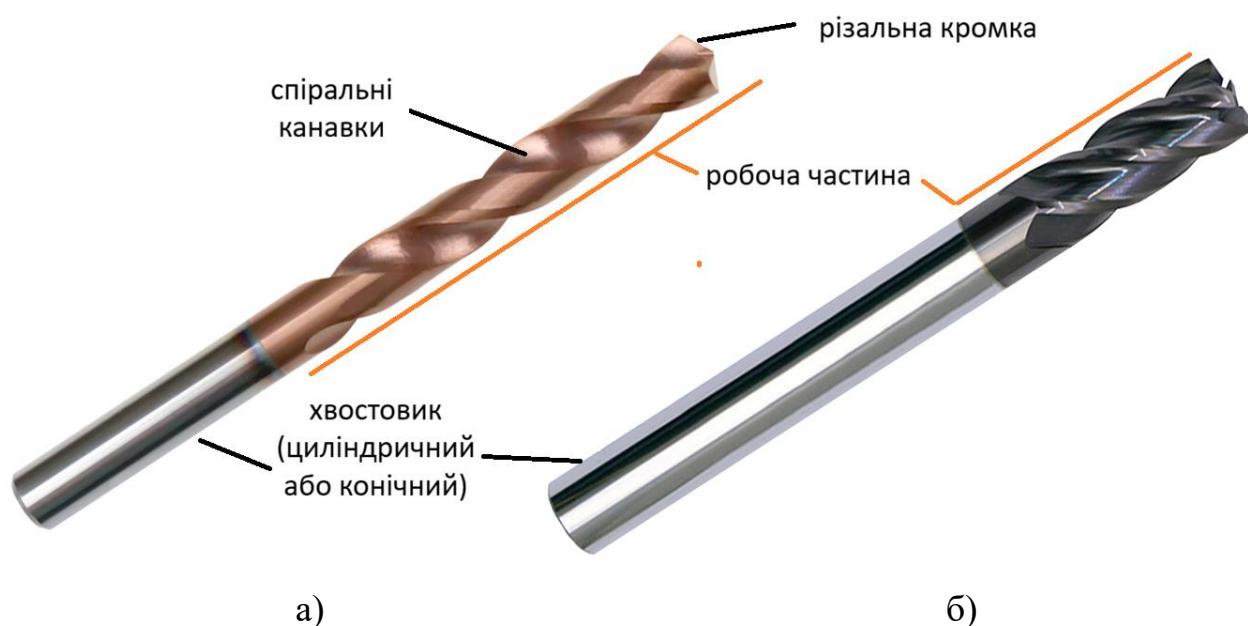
Конструктивні елементи спірального свердла (а) і фрези (б)
